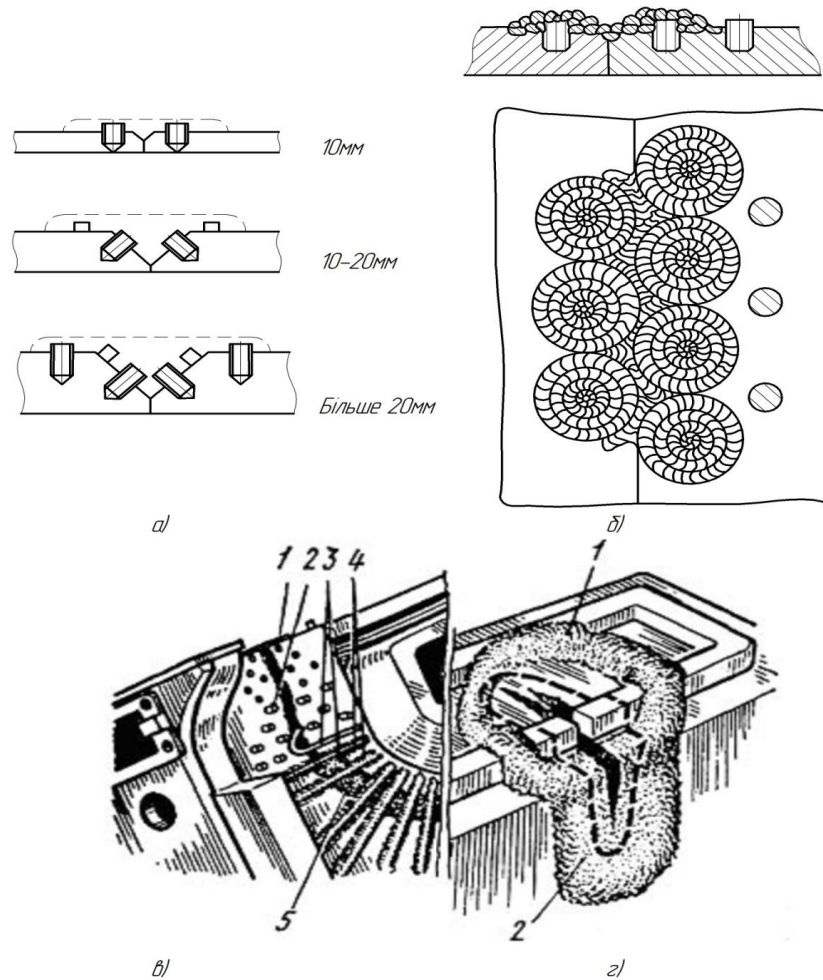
Зварювання чавуну з застосуванням сталевих шпильок:
